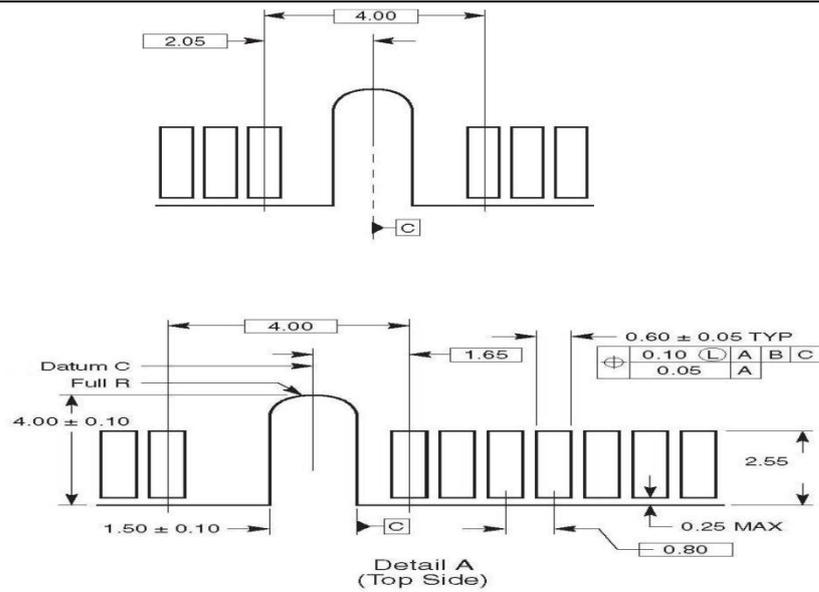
金手指 TOP 和 BOTTOM AB 处细节尺寸
